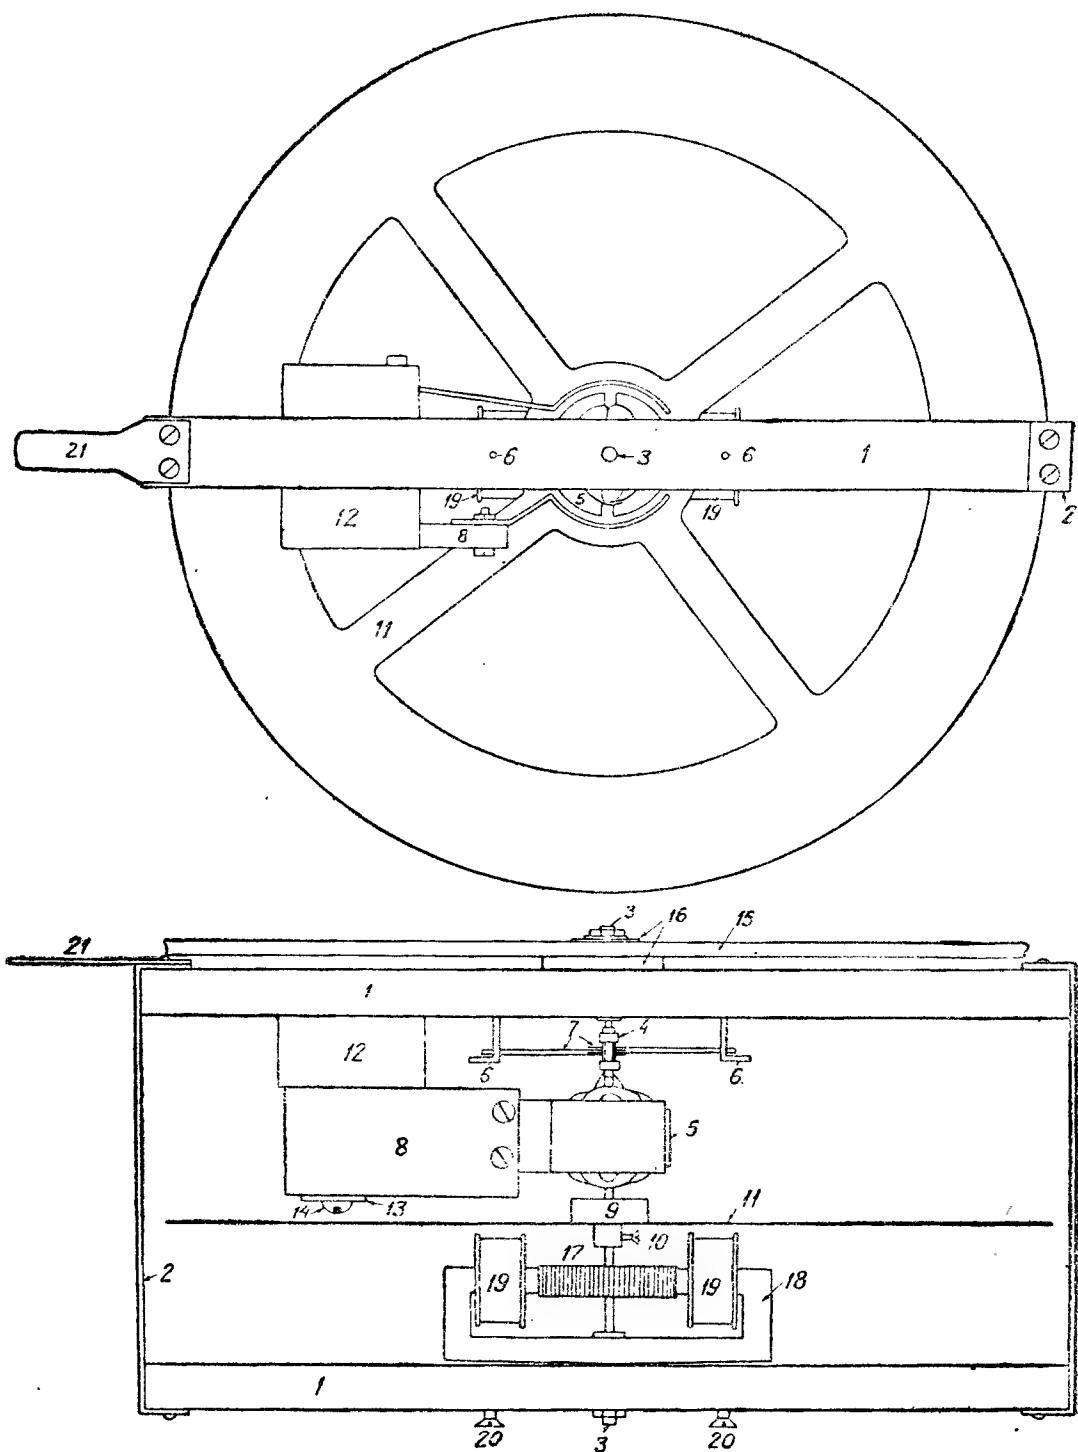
Сборка мотора первого варианта: 1 — деревянные планки, 2 — скобы, 3 — контакты, 4 — коллектор, 5 — якорь, 6 — щеткодержатель, 7 — щетки, 8 — магнит от УГ с полюсными наконечниками, 9 — деревянная втулочка, крепящая диск, 10 — шуруп, крепящий втулочку на оси, 11 — диск Нипкова, 12 — деревянная подкладка под магнит, 13 — латунная пластина, крепящая магнит, 14 — винт, крепящий магнит к планке, 15 — суконные шайбы для смягчения шума мотора, 16 — суконные шайбы для смягчения шума мотора, 17 — колесо Лакура, 18 — сердечник электромагнита, 19 — катушка электромагнита, 20 — шурупы для регулировки зазоров, 21 — рычажок установки в рамку
